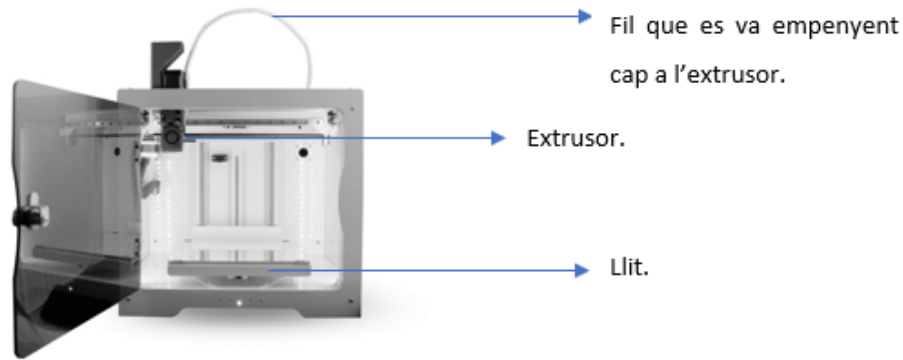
Impressora 3D, marca Tumaker, amb les parts més importants marcades.
